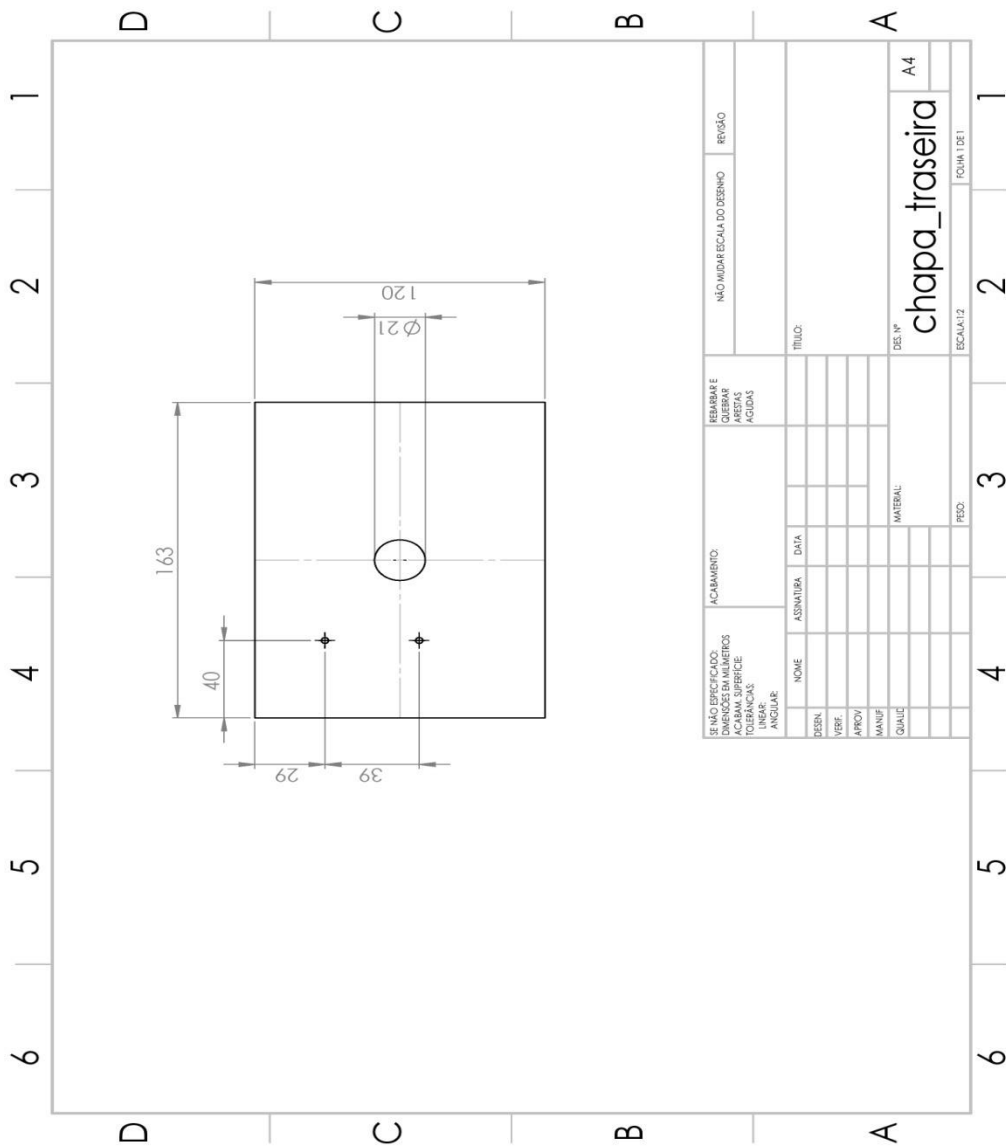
Desenho técnico da chapa traseira para a fixação do conector da tomada.
